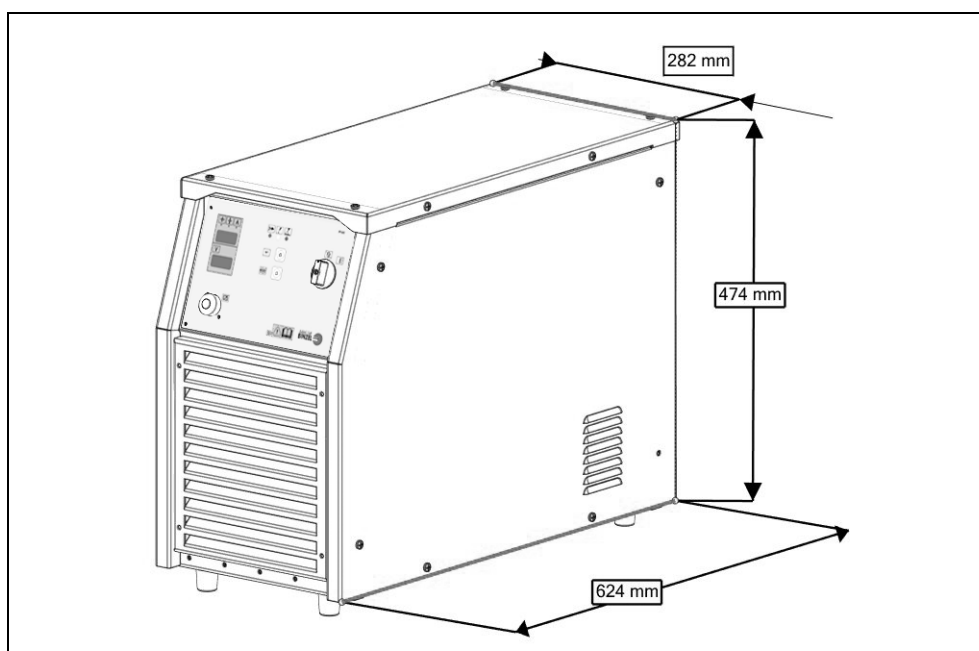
Dimensioni apparecchio robotizzato per la saldatura iROB Pulse
